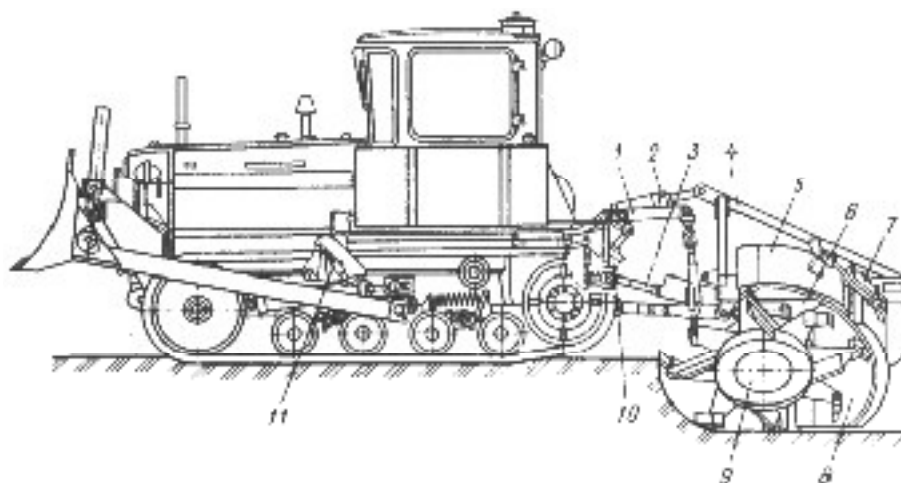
Схема плужно-фрезерного каналокопателя МК-23
